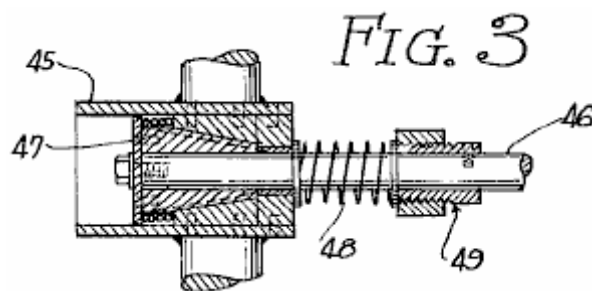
es una vista enfadada seccional tomada a lo largo de línea 3 - 3 de Fig.2 la exposición del mecanismo de encadenamiento de hélice en la posición ocupada;
